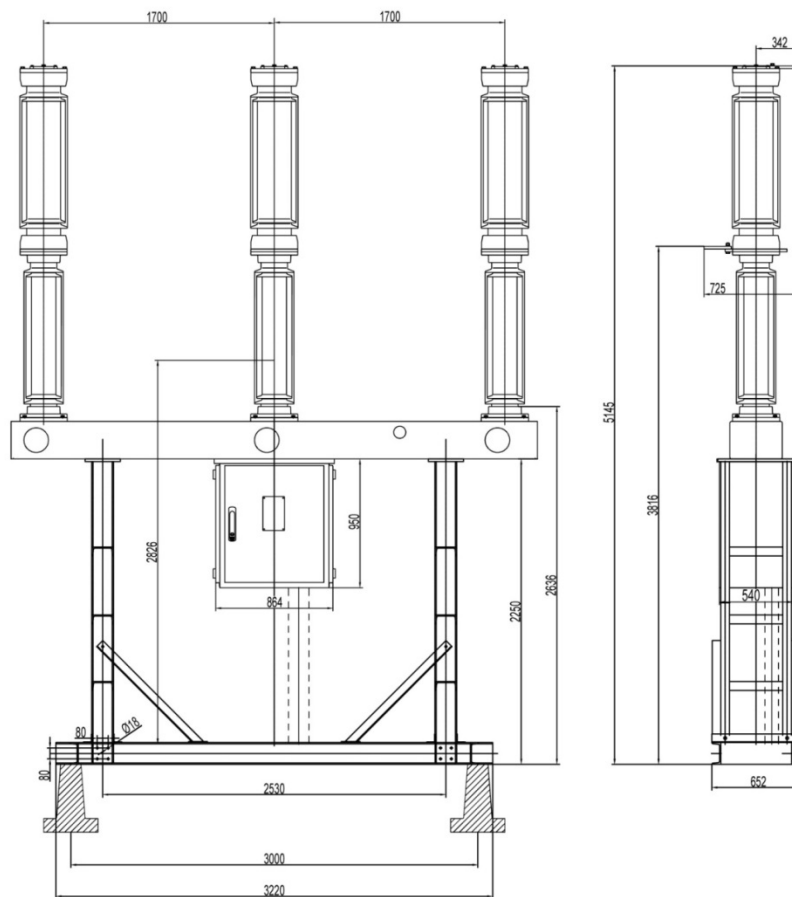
Габаритные размеры выключателя ВГН-КЕМ/kz напряжением 110 кВ
